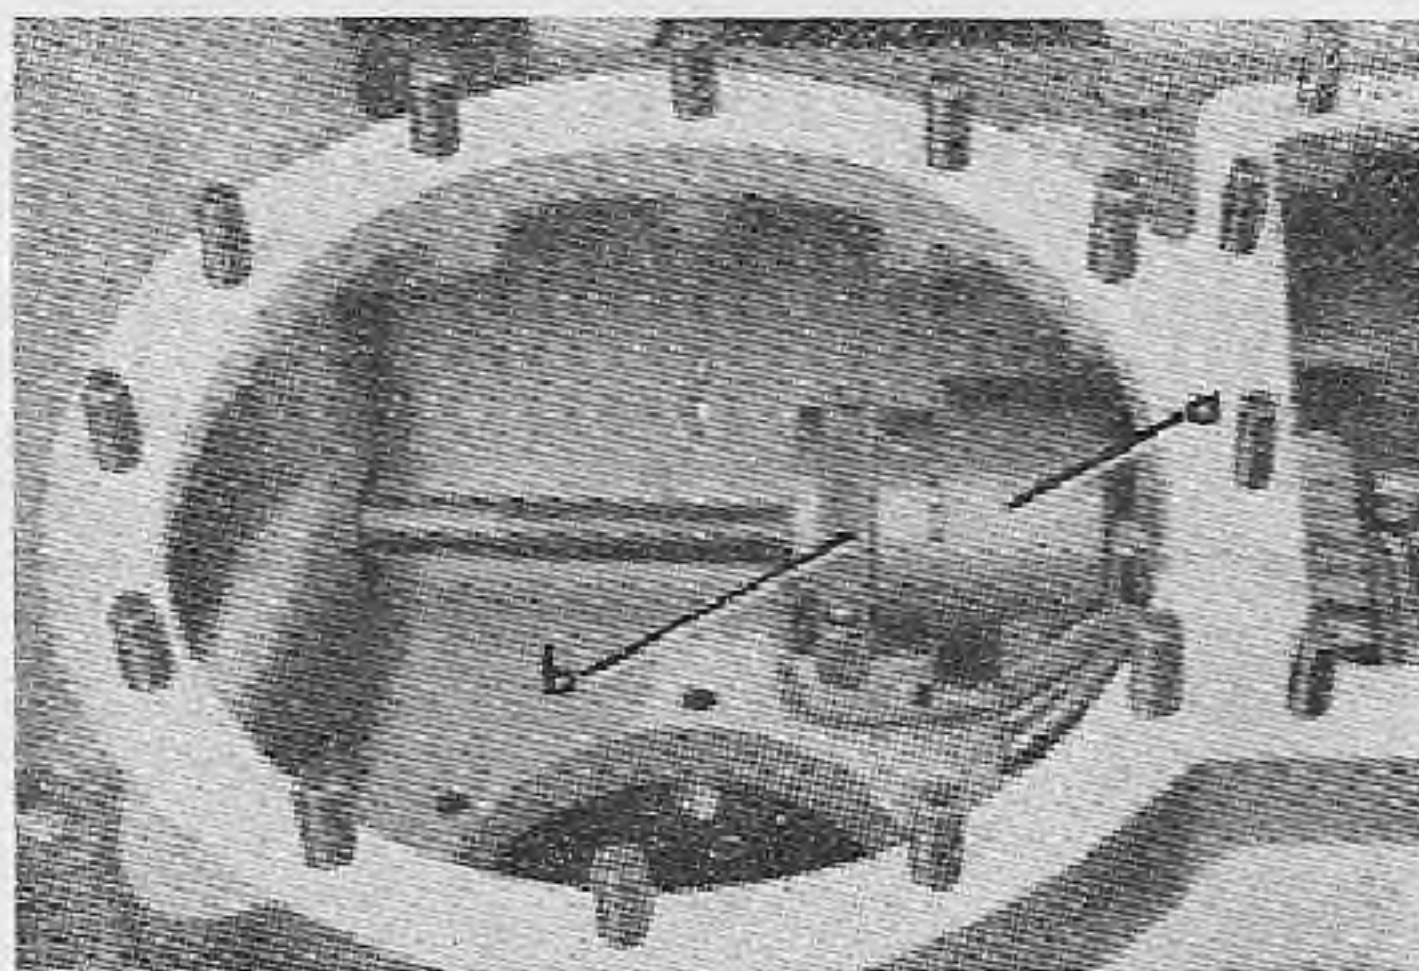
Desmontaje de la campana del mecanismo de rueda libre.
